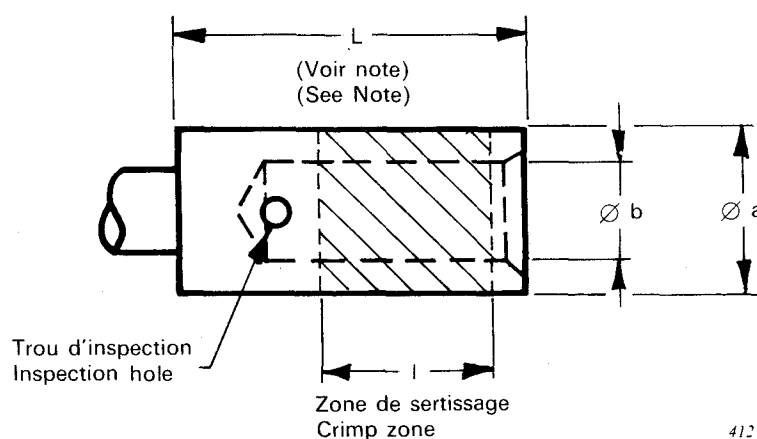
Conducteur intérieur — dimensions du fût de contact central à sertir.
